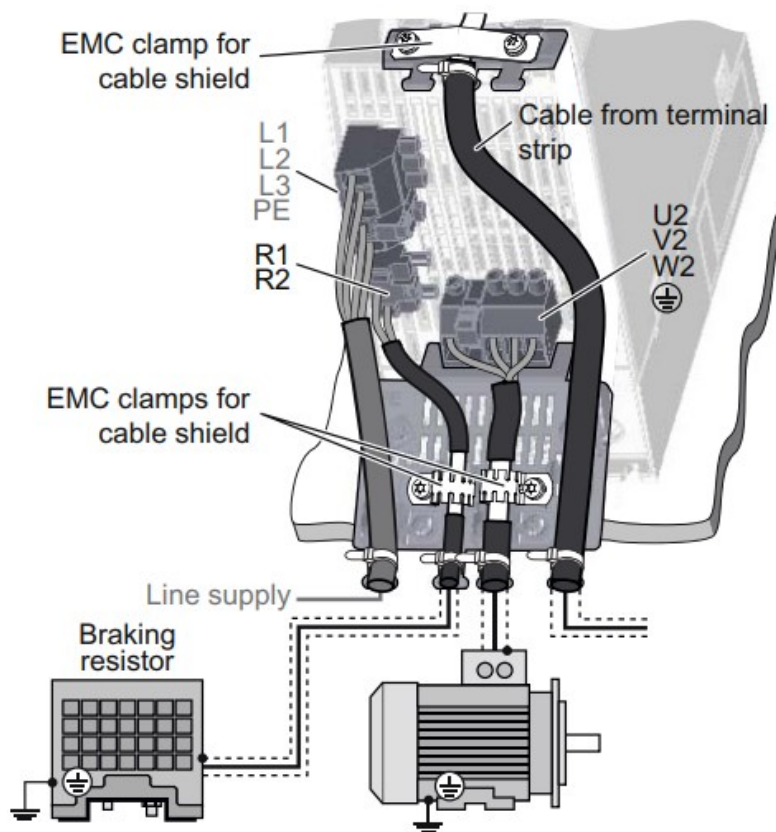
Fästplattans installationsinstruktion. (Siemens, 2014).
